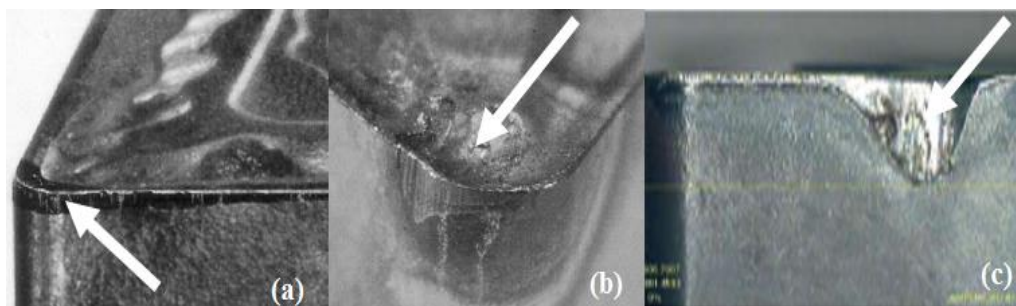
Formas de desgaste: (a) de flanco; (b) de cratera; (c) de entalhe.
